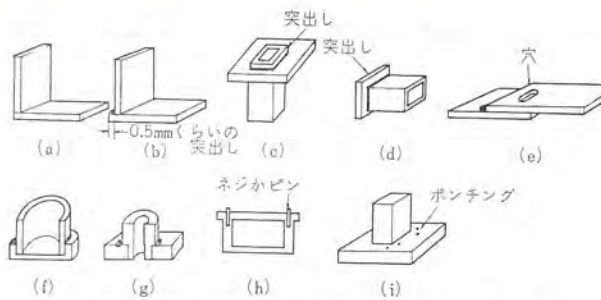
継手の形状 Fig. 3.7 Shape of joints.
